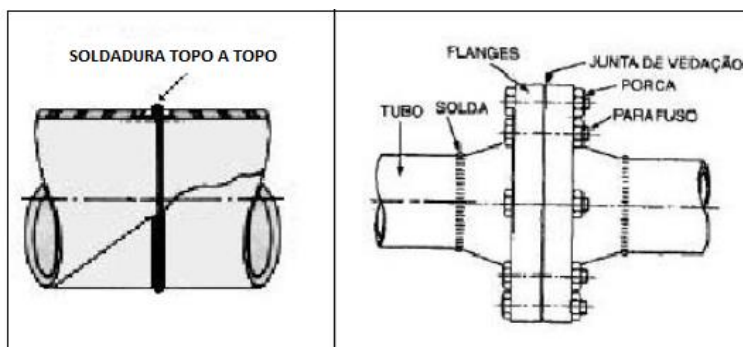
Soldadura topo a topo e ligação flangeada
